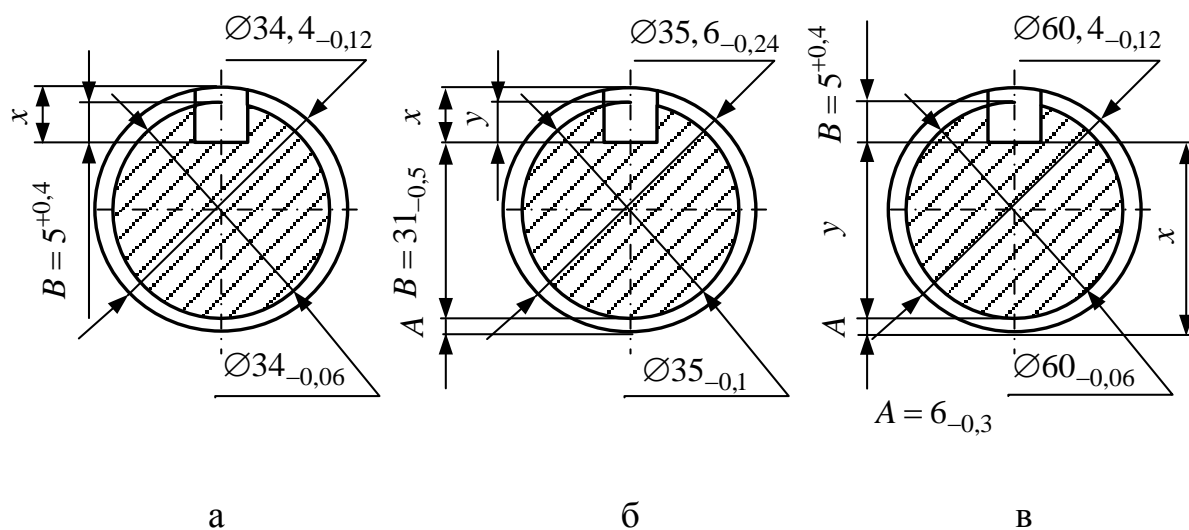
Размеры шпоночного вала с учетом припуска на обработку по цилиндрической поверхности
